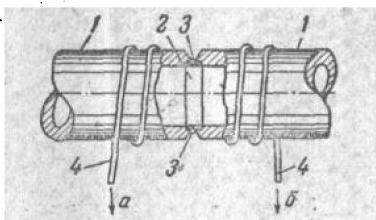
利用螺管线圈磁化管子焊接接头以检查第一道焊缝上的裂纹：
